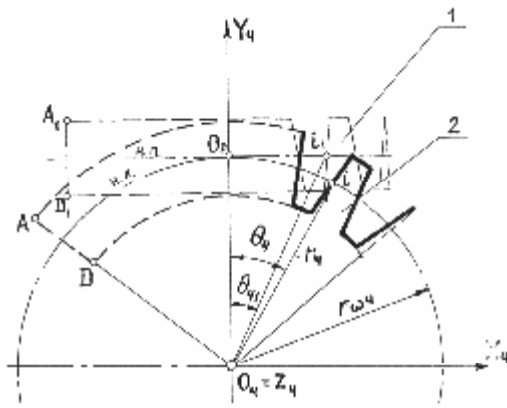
Схема формирования погрешностей при несовпадении профиля рейки и цилиндрической поверхности основного червяка
